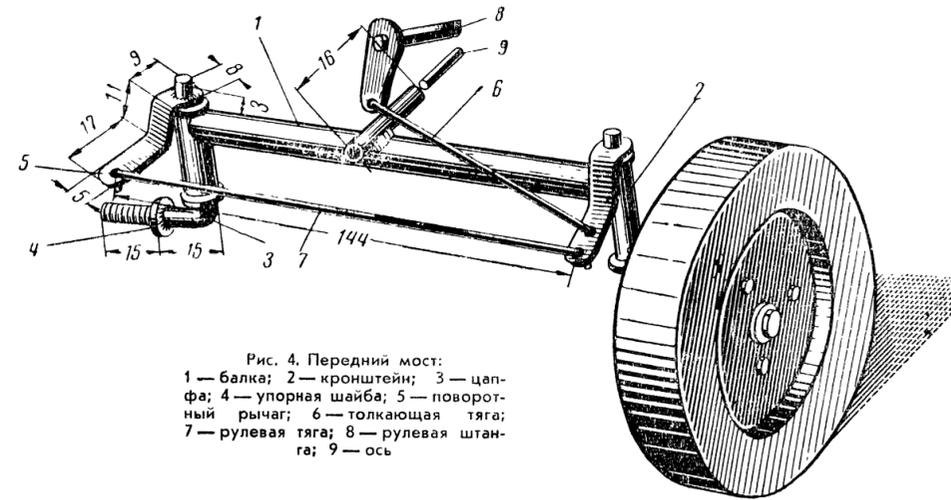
Передний мост: 1—балка; 2—кронштейн; 3—цапфа; 4—упорная шайба; 5—поворотный рычаг; 6—толкающая тяга; 7—рулевая тяга; 8—рулевая штанга; 9—ось
